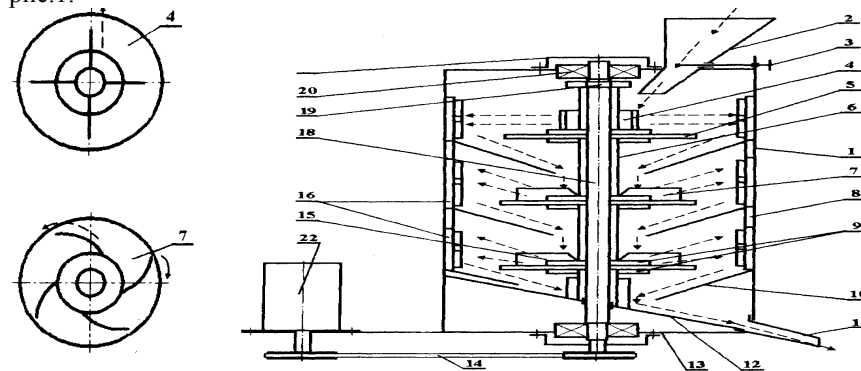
Схема устройства скарификатора семян бобовых трав: 1 – корпус; 2 – засыпная горловина; 3 – задвижка регулировки потока семян; 4 – крыльчатка прямая, крестообразная для равномерного распределения семян; 5 – диск наждачный; 6 – распорная втулка; 7 – крыльчатка изогнутая для скольжения семян; 8 – распорная втулка распределителей семян; 9 – фланцы; 10 – распределитель семян; 11 – съемный лоток; 12 – скатывающий лоток; 13 – основание; 14 – ременная передача; 15 – направляющие канавки; 16 – ленты наждачные для скарификации семян; 17 – распорная втулка; 18 – вал; 19 – зажимная гайка; 20 – подшипник; 21 – крышка подшипника; 22 – электродвигатель 1000 об/мин, 2 кВт
